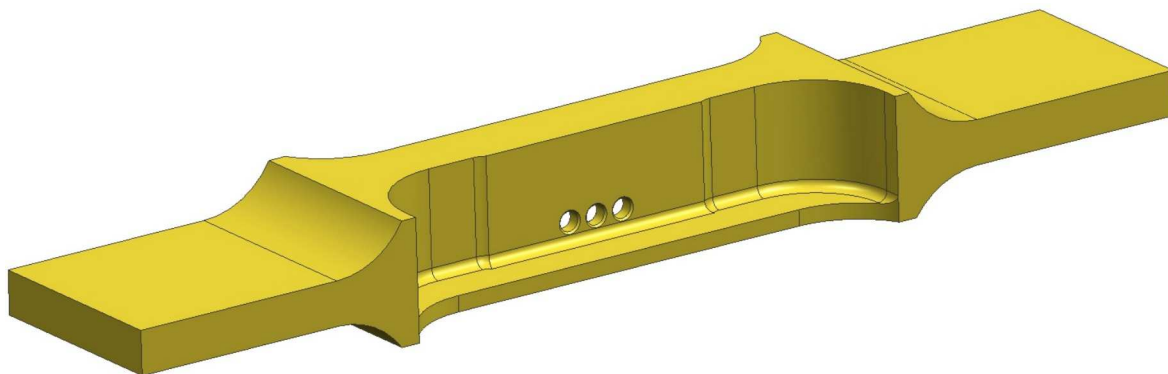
Трехмерная модель конструктивно-подобного образца стрингера для проведения усталостных испытаний
